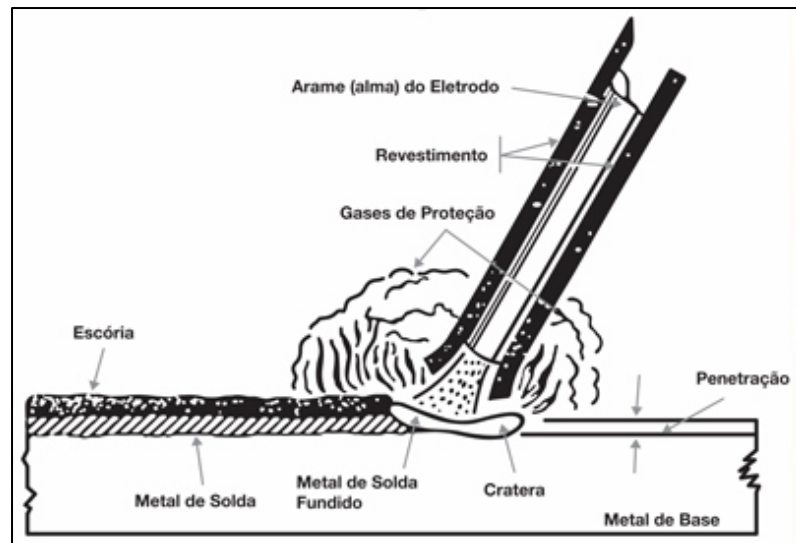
Processo de Soldagem MMA/SMAW - Eletrodo Revestido
